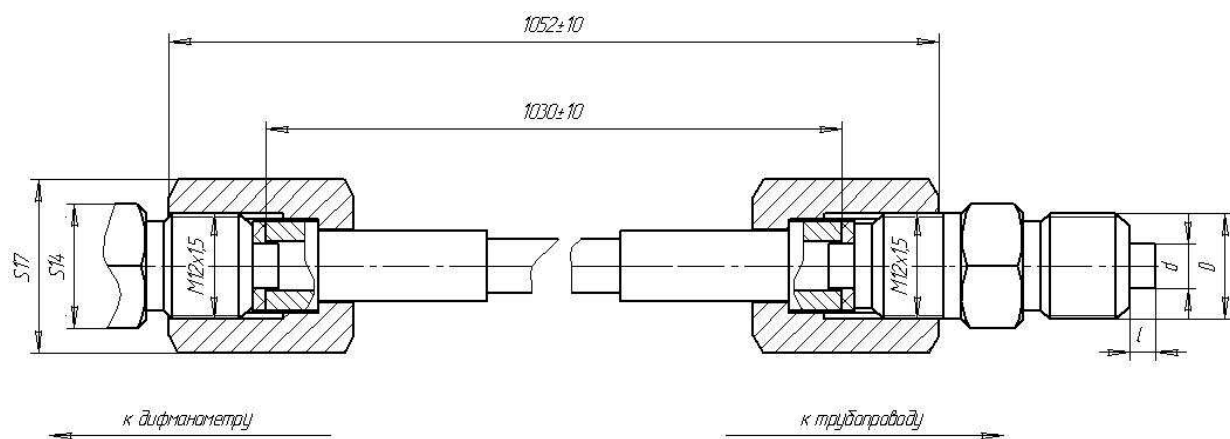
Габаритные и присоединительные размеры дифманометра
